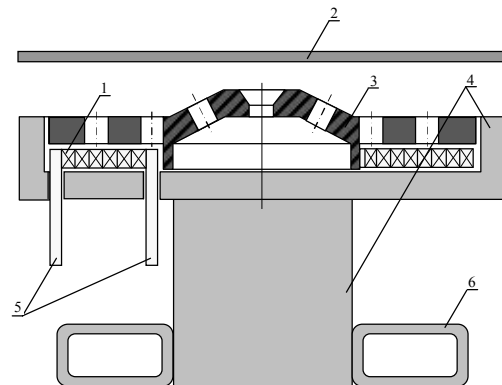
Конструкторский эскиз инструмента внешней магнитно-импульсной рихтовки на основе совмещенного дискового СУ с заготовкой: 1 – витки плоской спирали первичной обмотки импульсного трансформатора; 2 – тонкостенная металлическая заготовка; 3 – индуктор-инструмент с внутренним отверстием в форме усеченного конуса; 4 – диэлектрический каркас; 5 – электрические выводы первичной обмотки импульсного трансформатора; 6 – держатель инструмента
